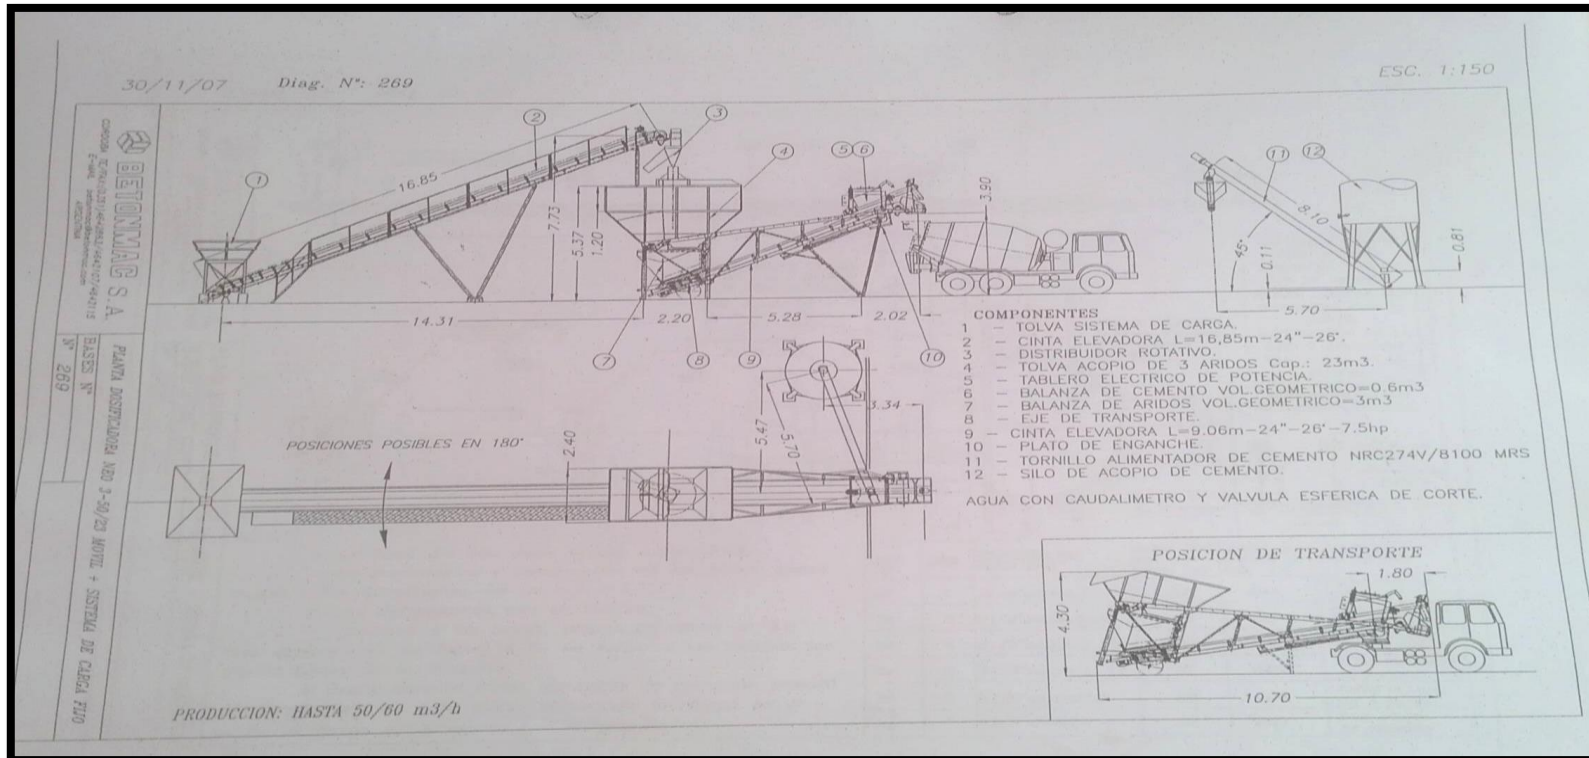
Esquema de la Planta Bentonmac de Producción de Concreto Premezclado.
